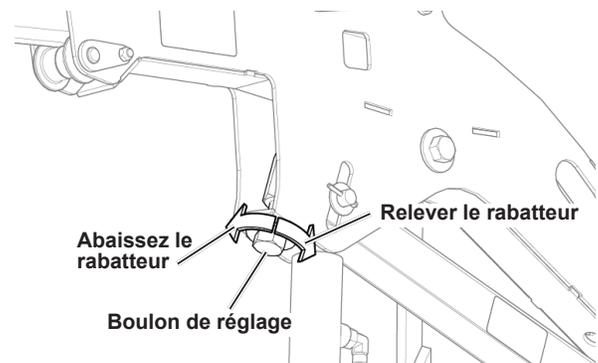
Réglage de la hauteur du bras du rabatteur central
